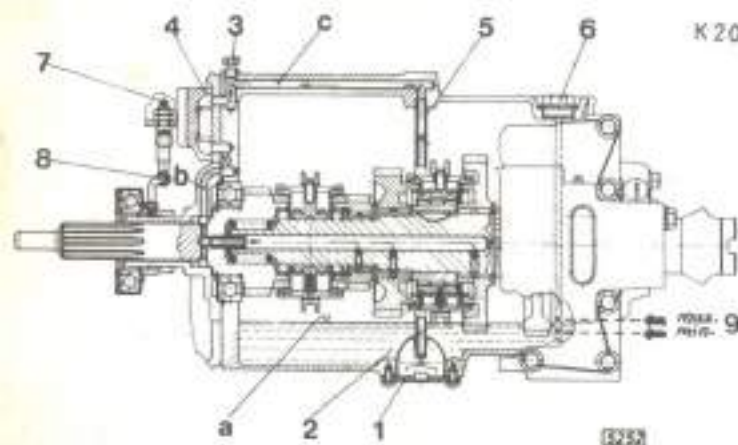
Схема смазки для коробки передач АШН-75 (К20-90)
